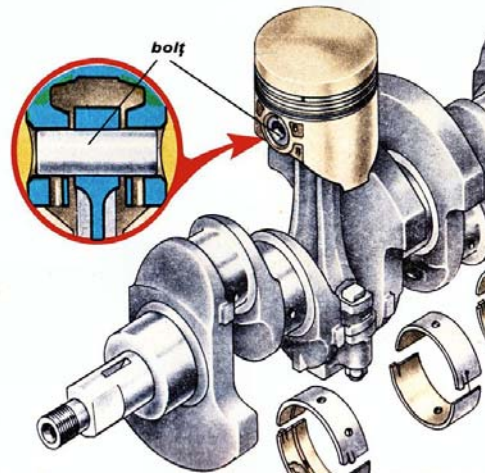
Detaliu mecanismului arbore cotit – bielă – piston - cilindru [9]
